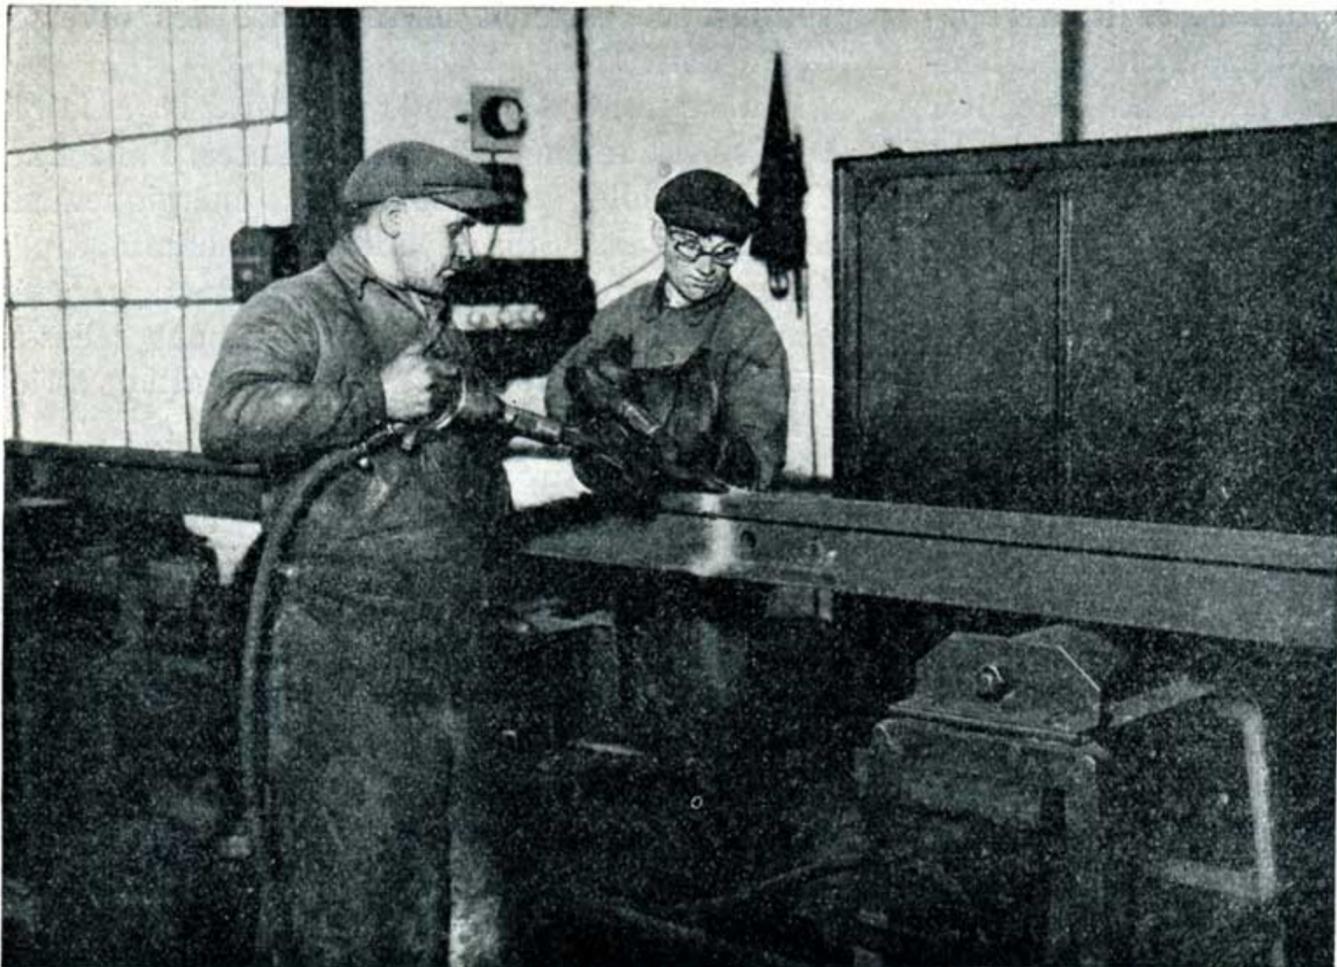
Mise sous profil d'un joint immédiatement après soudure.
